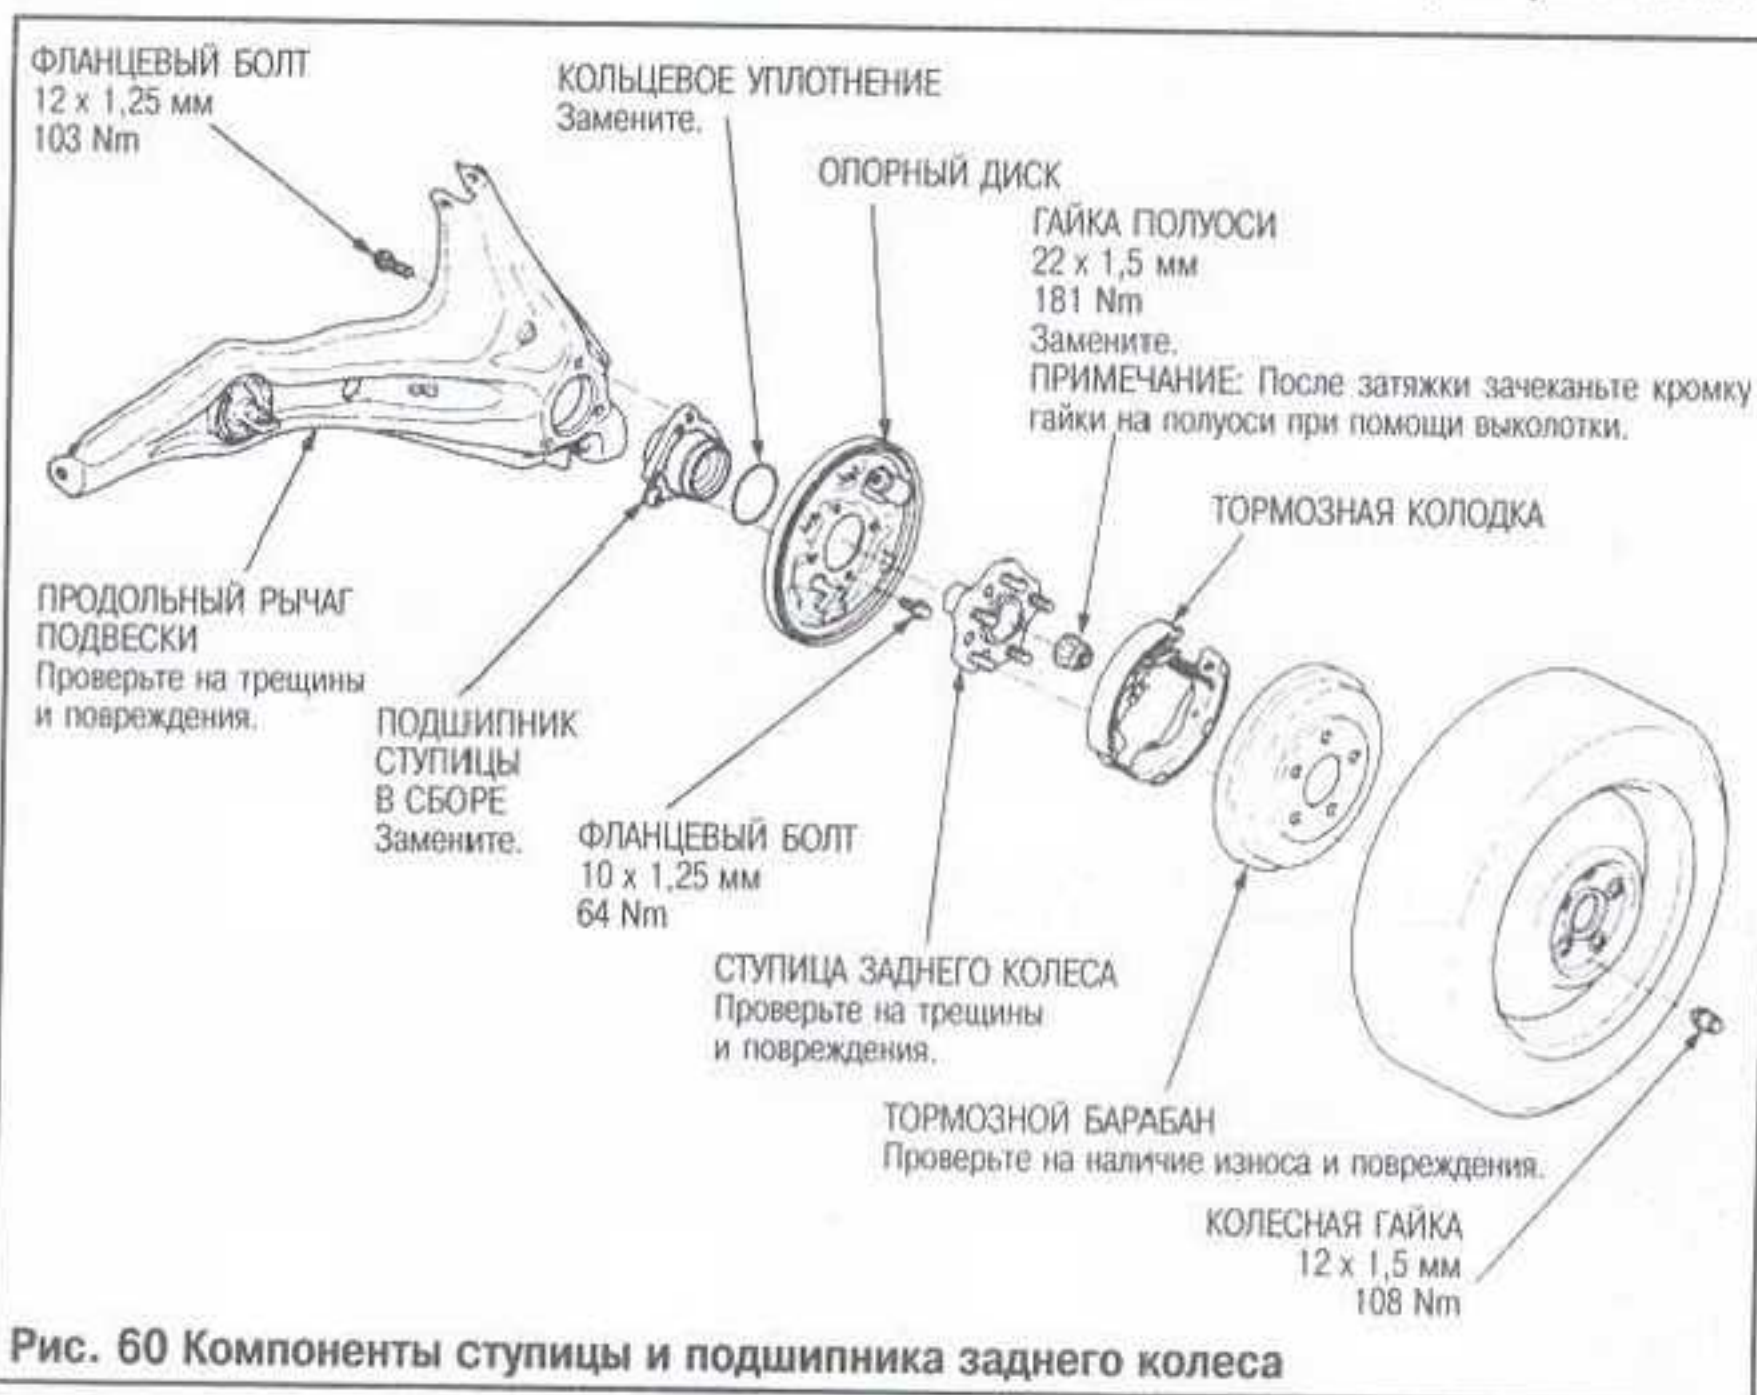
Компоненты ступицы и подшипника заднего колеса
